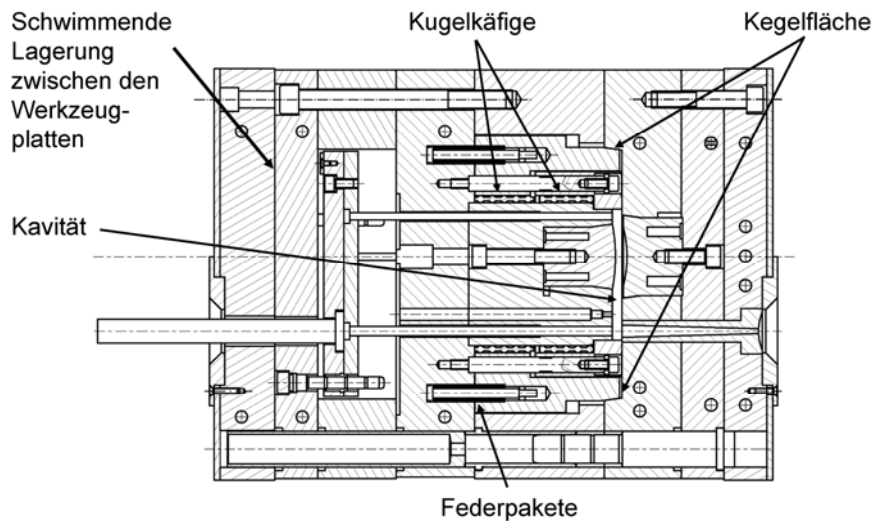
Schnitt durch das Werkzeug mit federnd gelagertem Zentrierring
